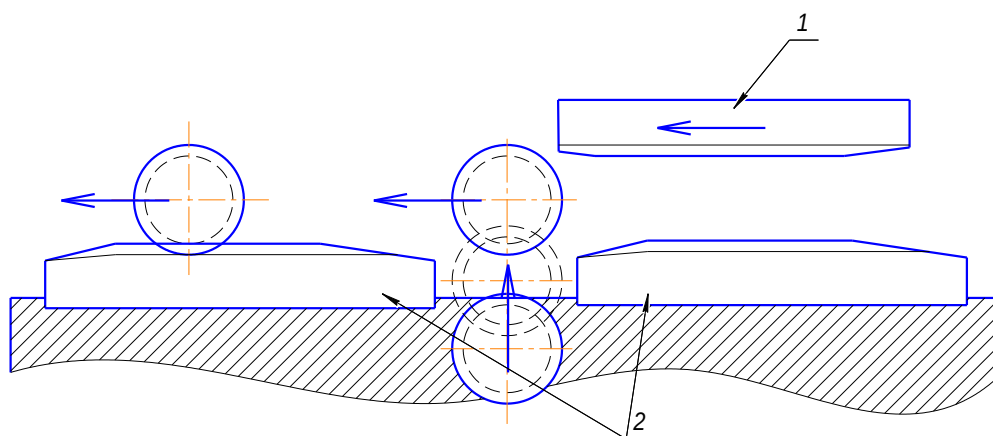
а – Накатывание тремя плашками. Прямой ход: 1 – подвижная плашка, 2 – неподвижные плашки
